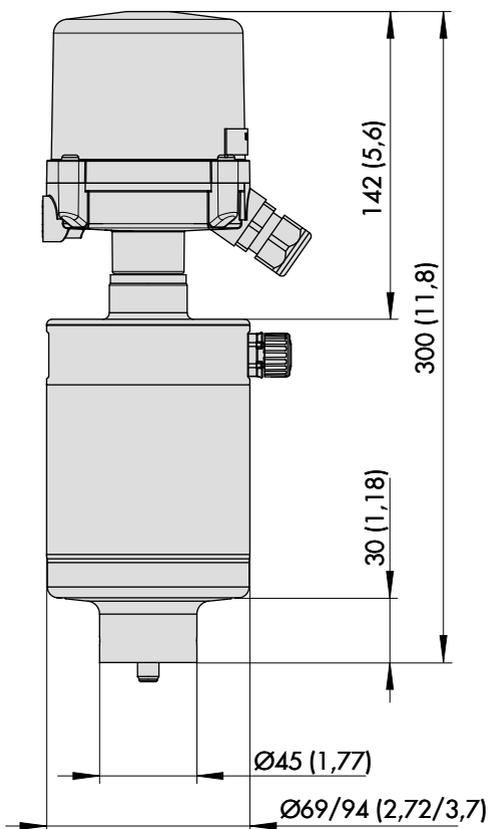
Plan coté du servomoteur type 3379-02
